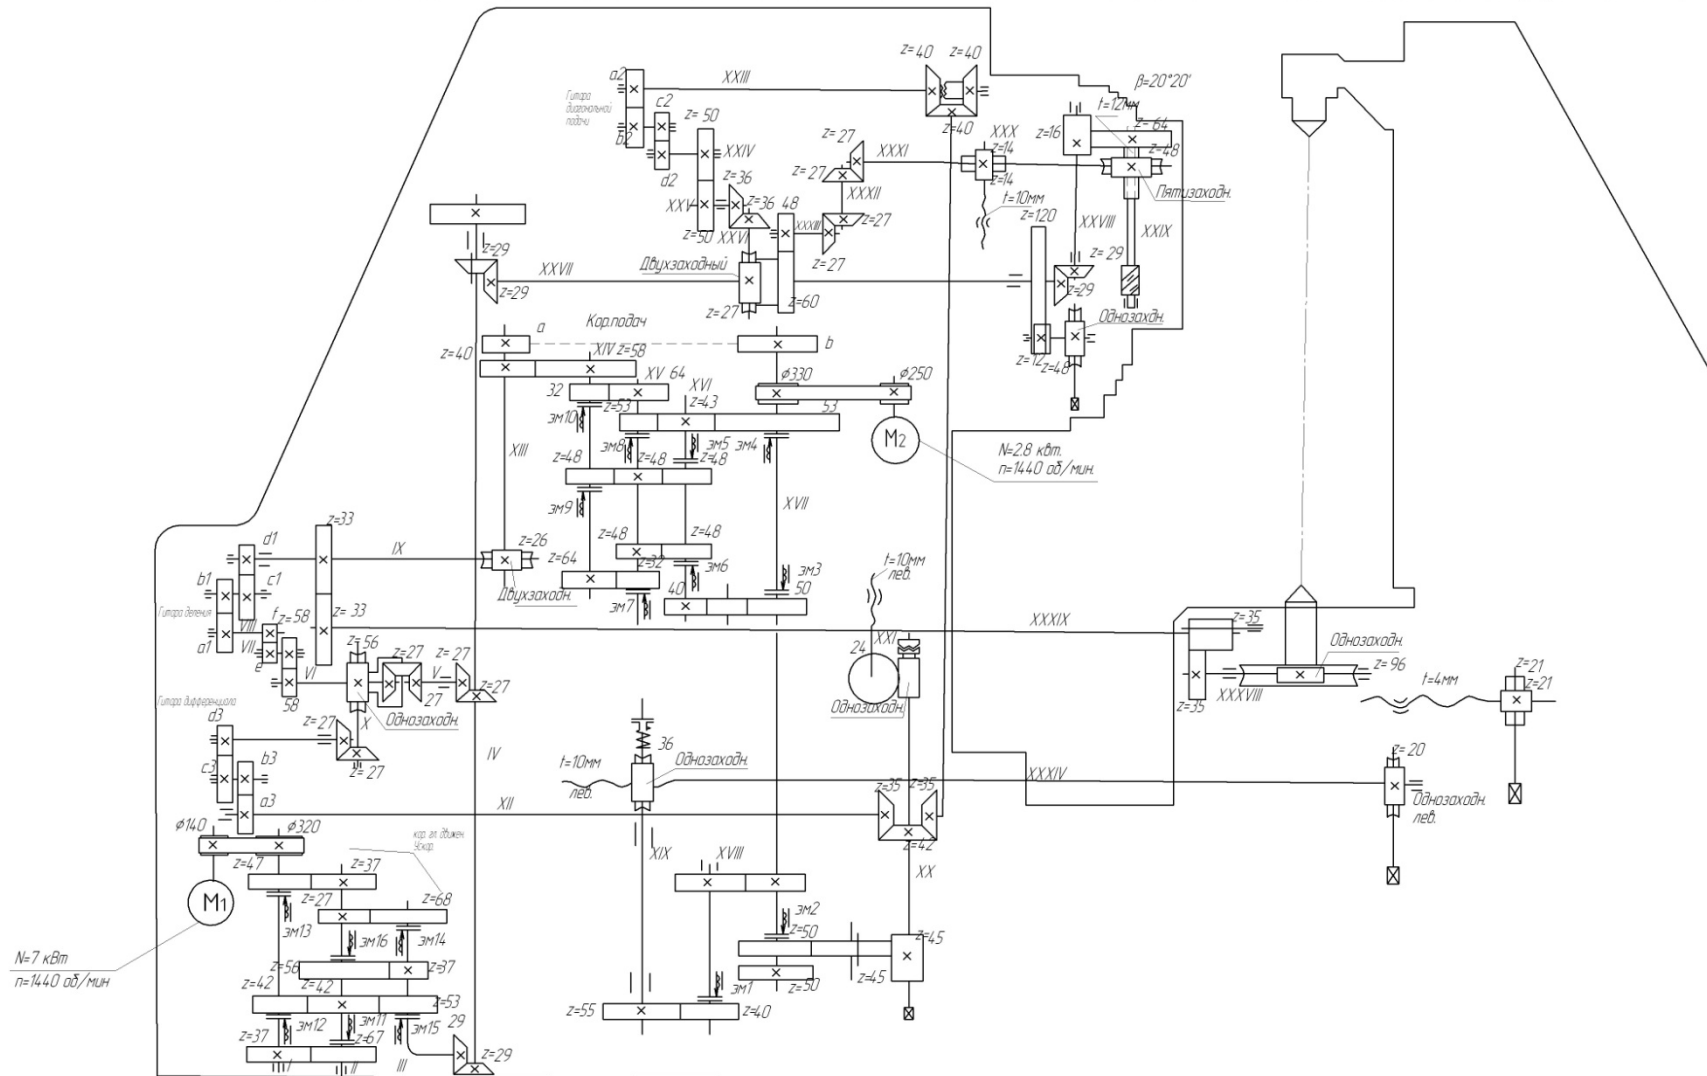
Кинематическая схема зубофрезерного станка модели 5К324
